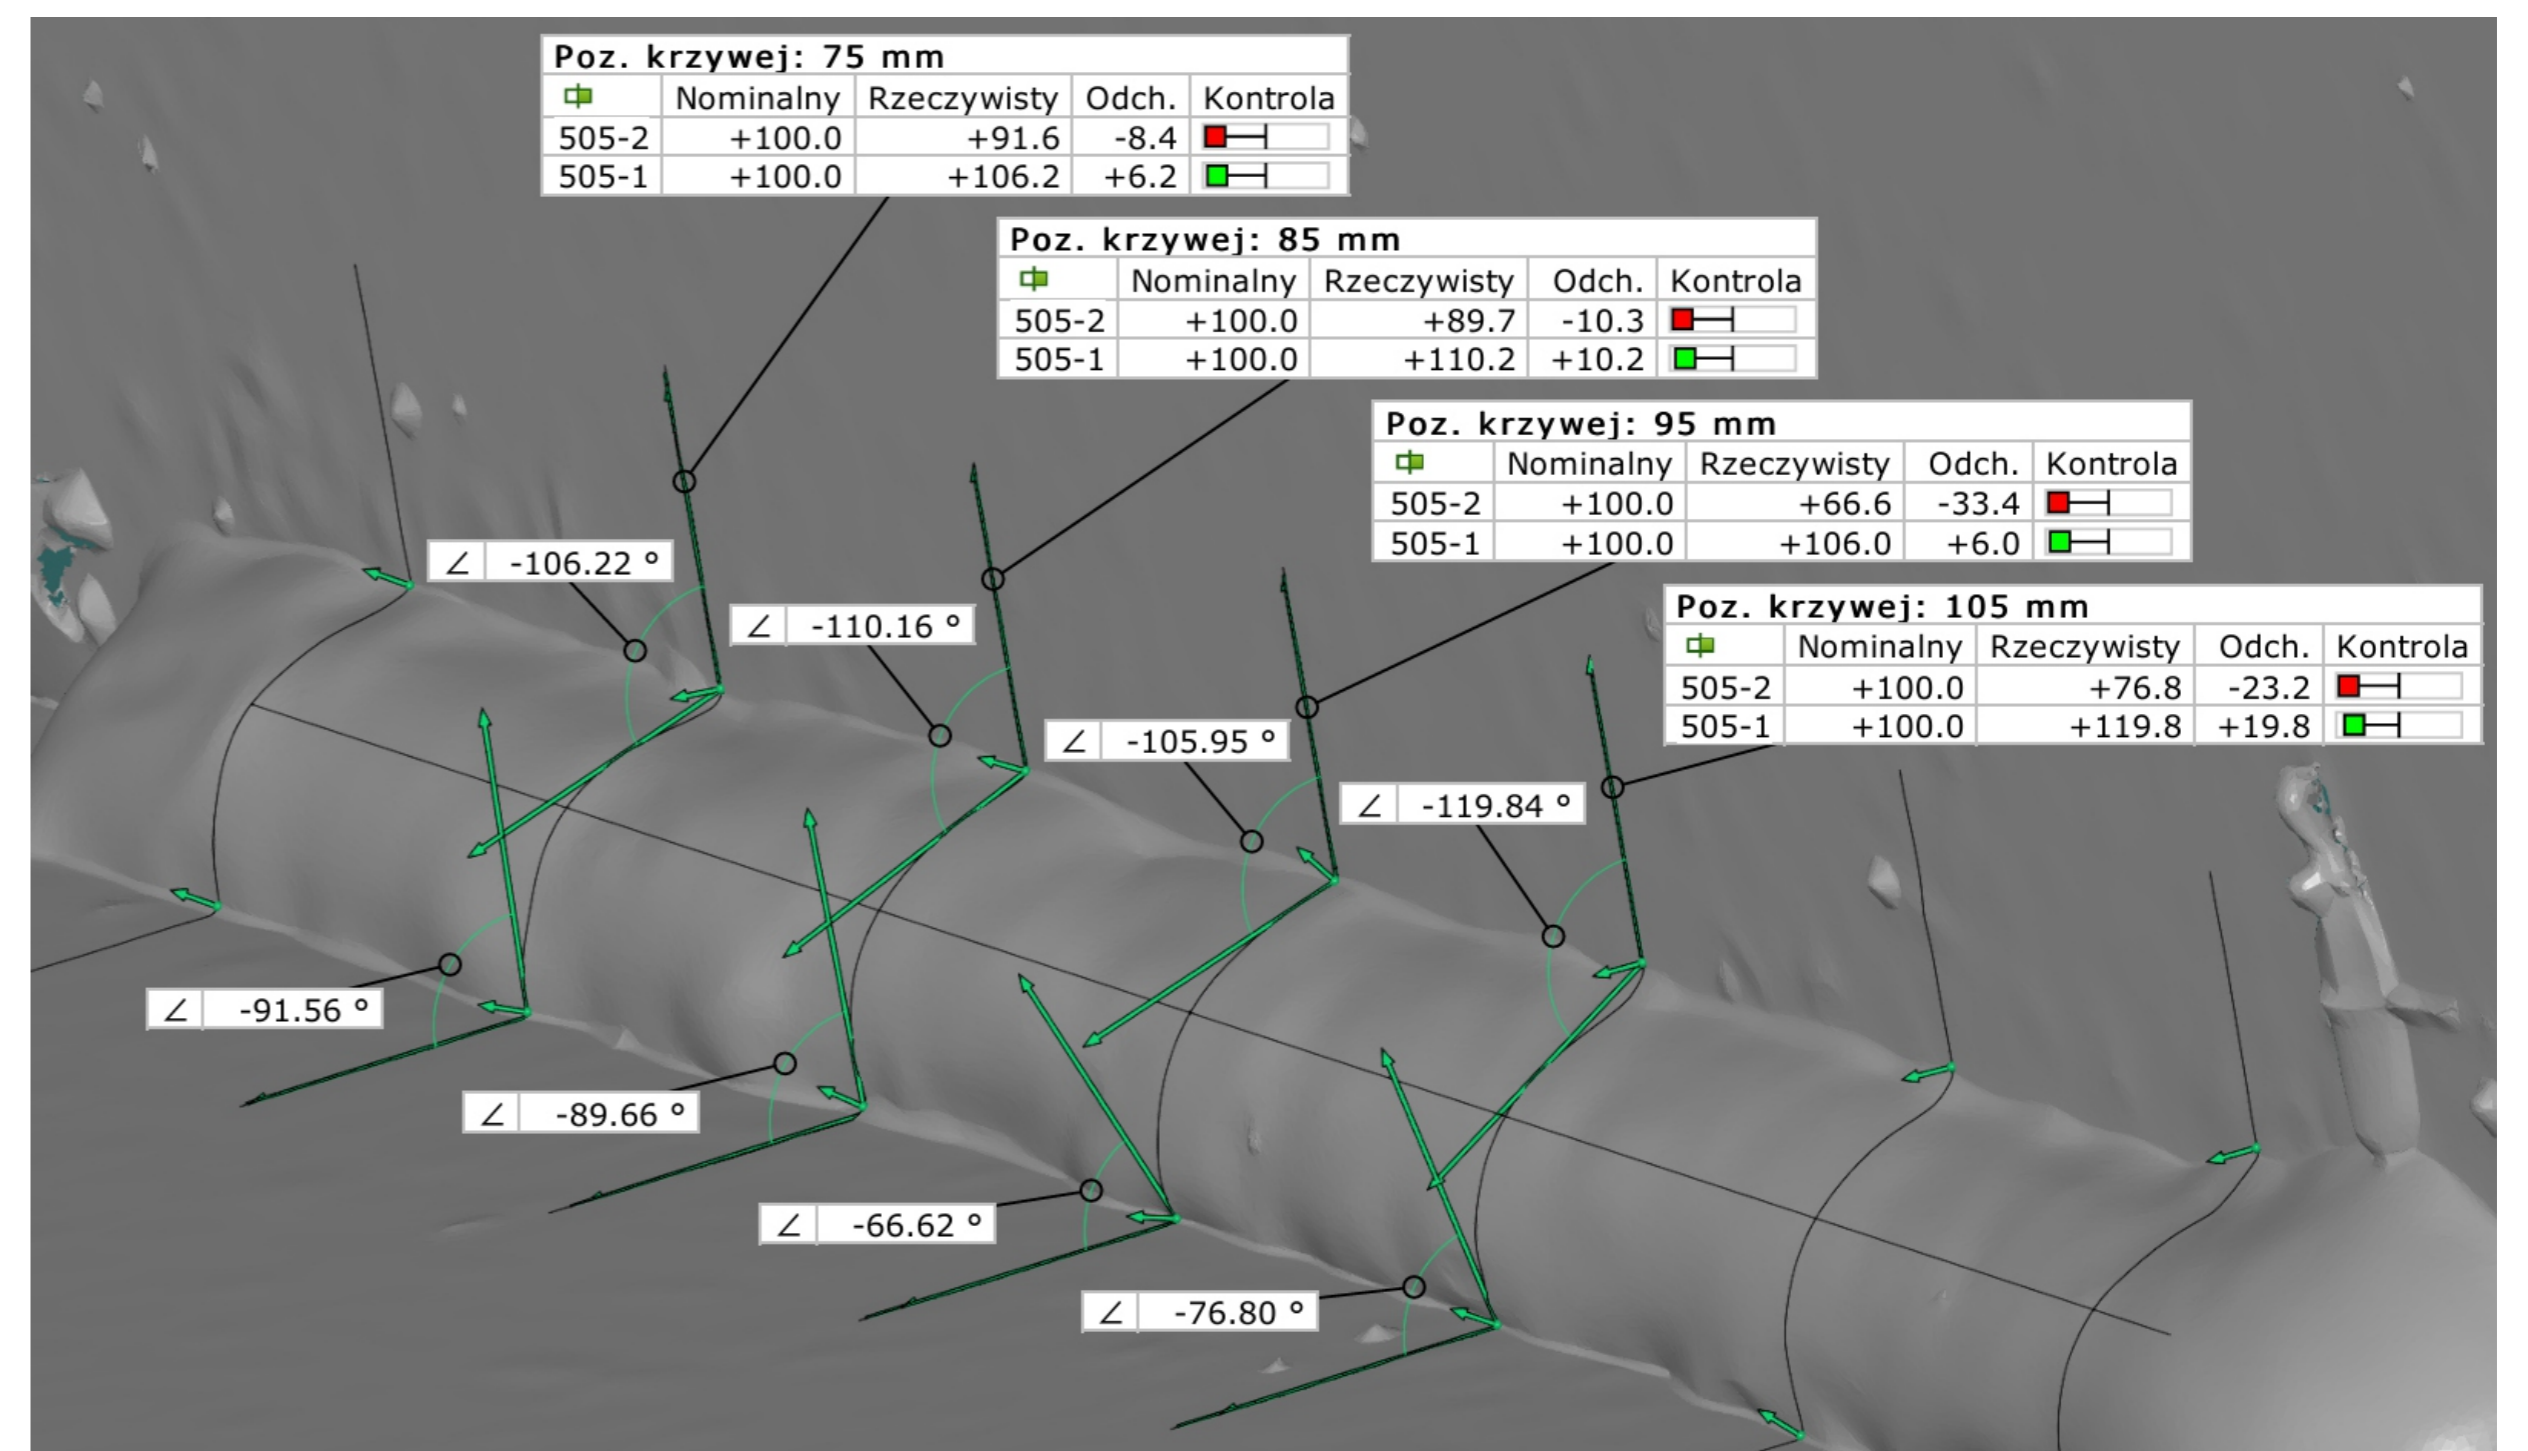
Widok okna tworzenia przekrojów spoiny w oprogramowaniu Weld Check
